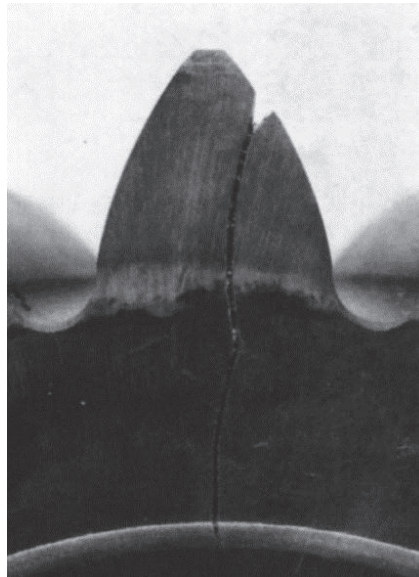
Fractura a través de una grieta en la cara del diente.
